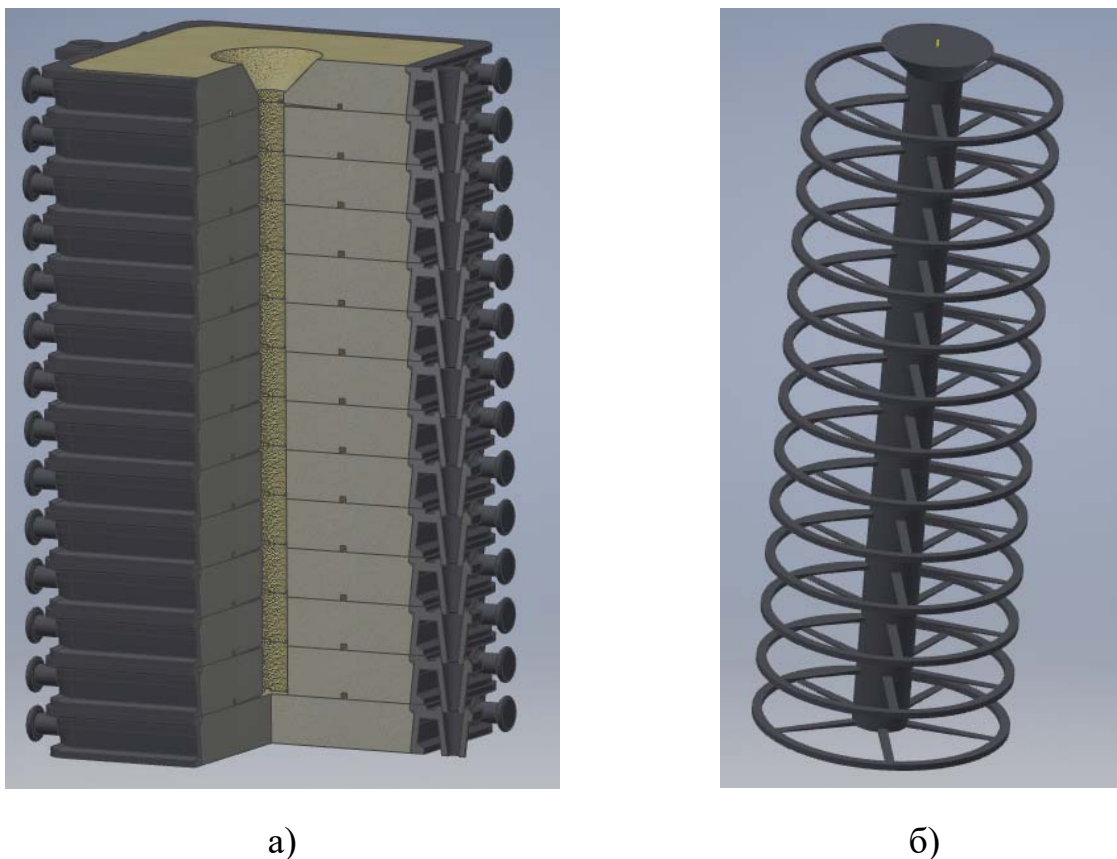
Стопка опок в сборе (а) и получаемая отливка (б)
